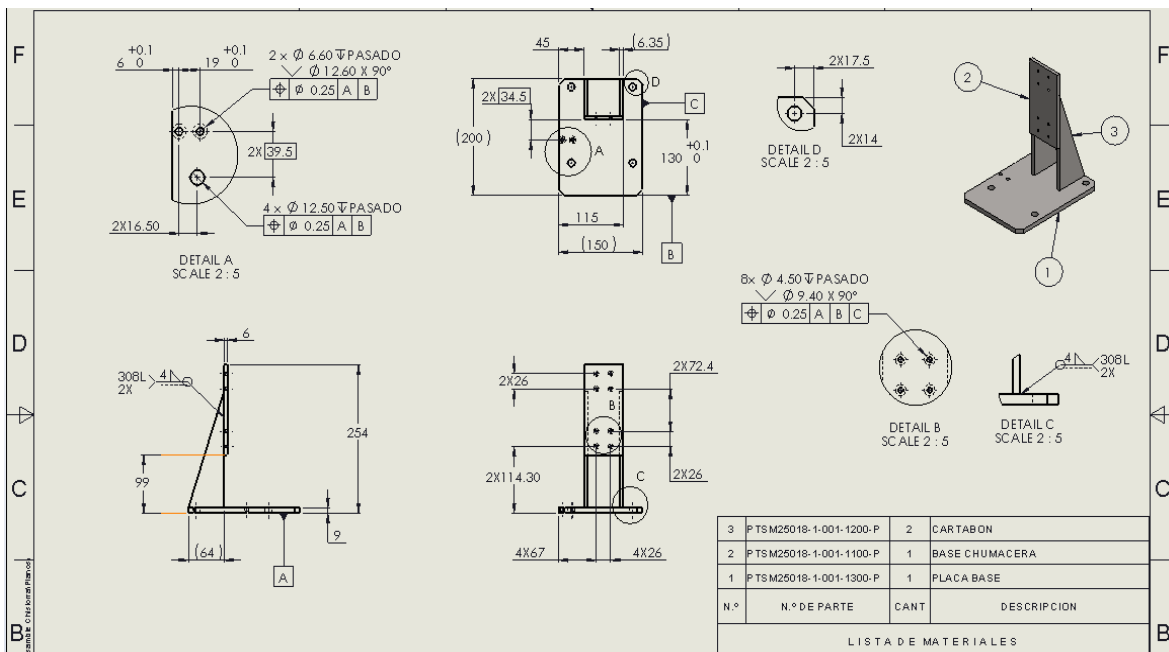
Sub-ensamble soldadura. Base soldada.
